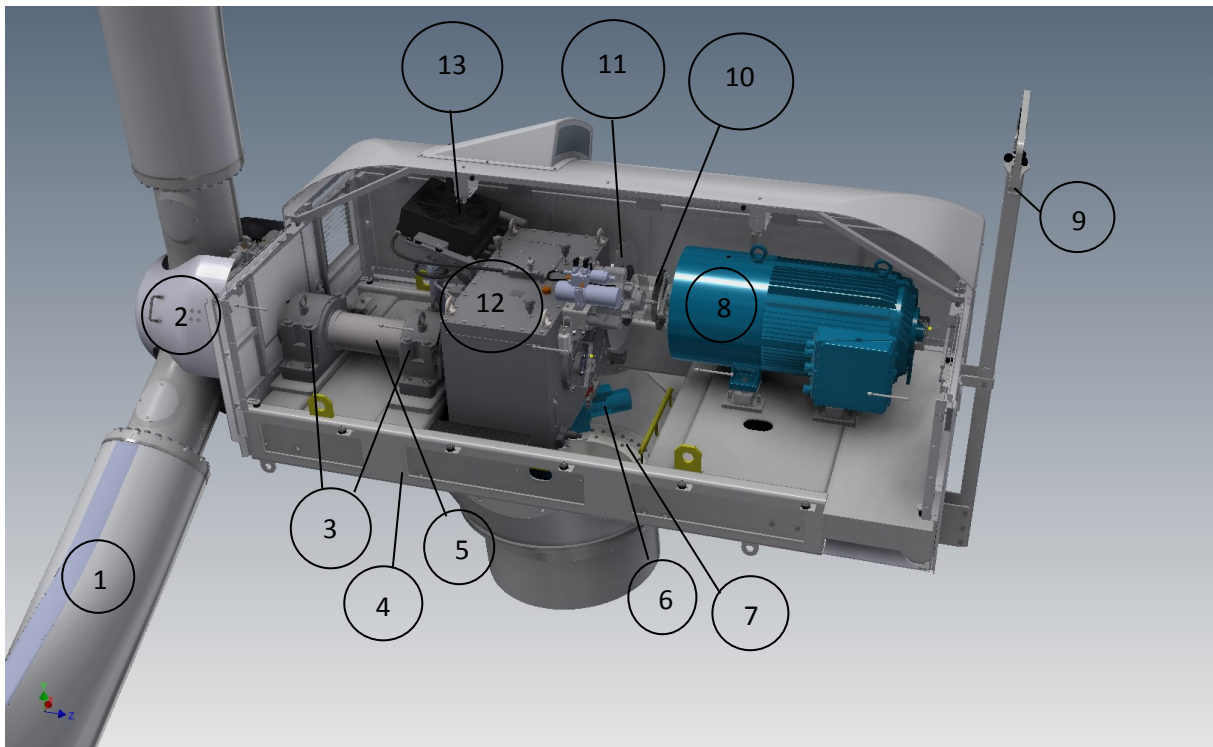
Übersichtszeichnung des Maschinenhauses
